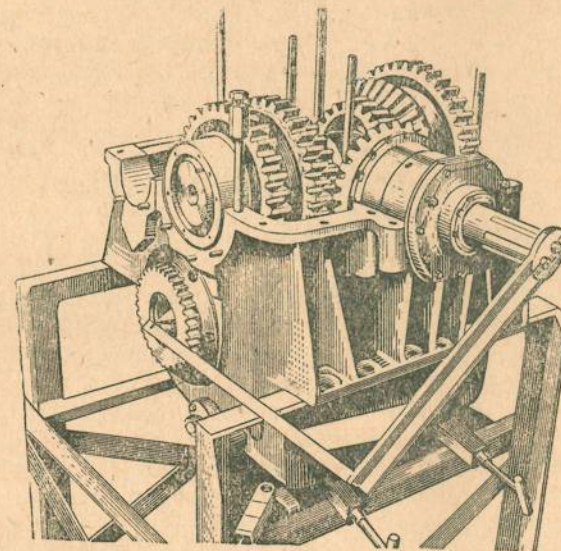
Проверка размера и подбор прокладок на торец ведущего вала коробки перемены передач
